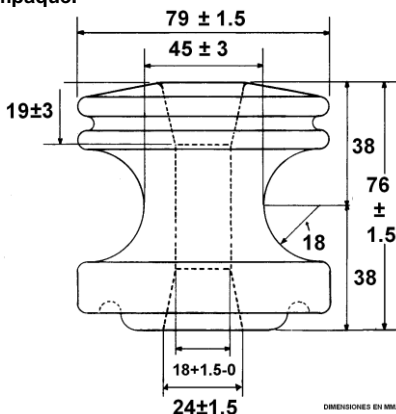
Especificaciones generales para Aislador tipo Carrete 53-2 AC
